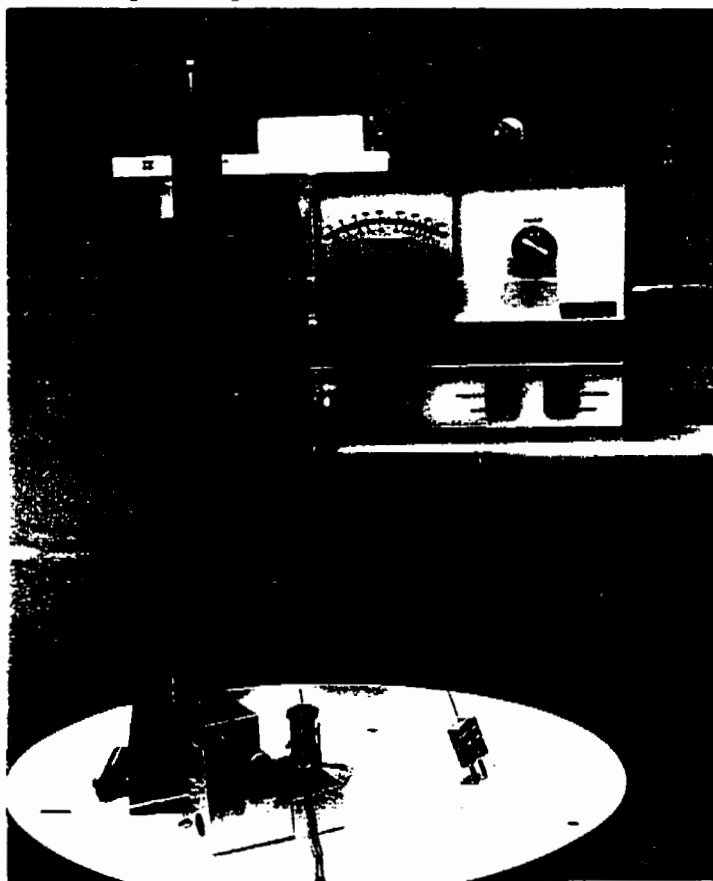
Montage pour souder sur le dessus de l'éprouvette
